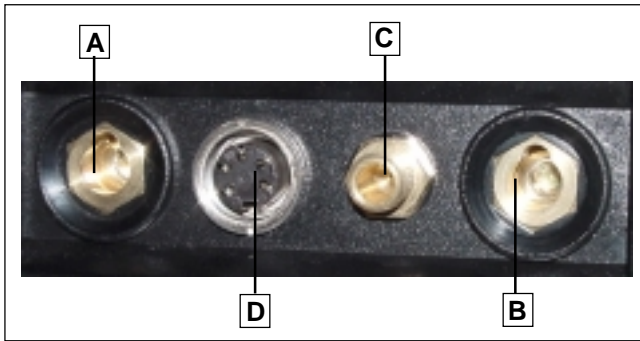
Brenner- bzw. Schweißkabelanschlüsse an der Geräte-Frontseite
